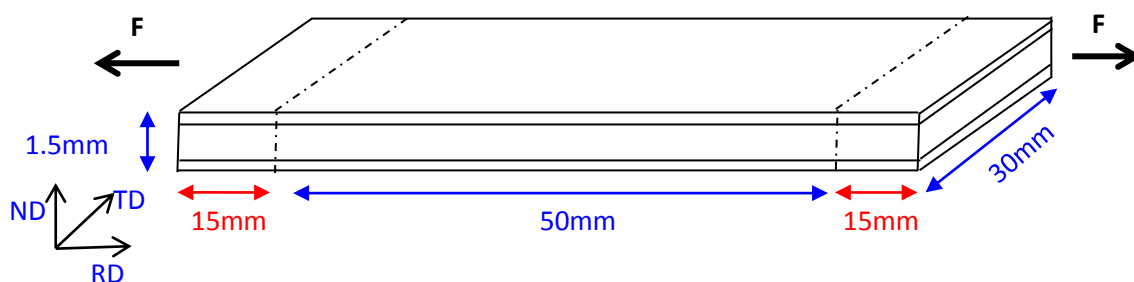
Dimensions des éprouvettes de traction pour les échantillons avec le revêtement Zn.
